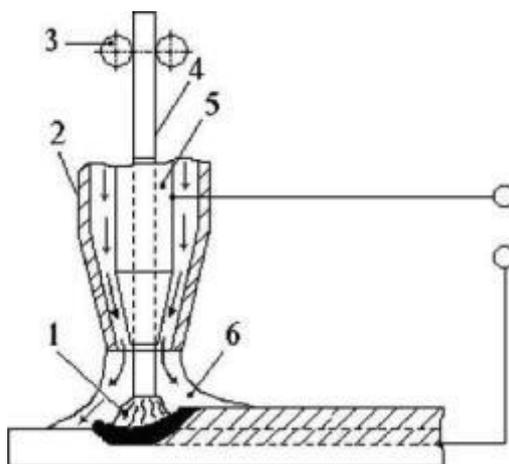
Дуговая сварка в защитном газе плавящимся электродом: 1 – электрическая дуга; 2 – газовое сопло; 3 – подающие ролики; 4 – электродная проволока; 5 – токоподводящий мундштук; 6 – защитный газ
